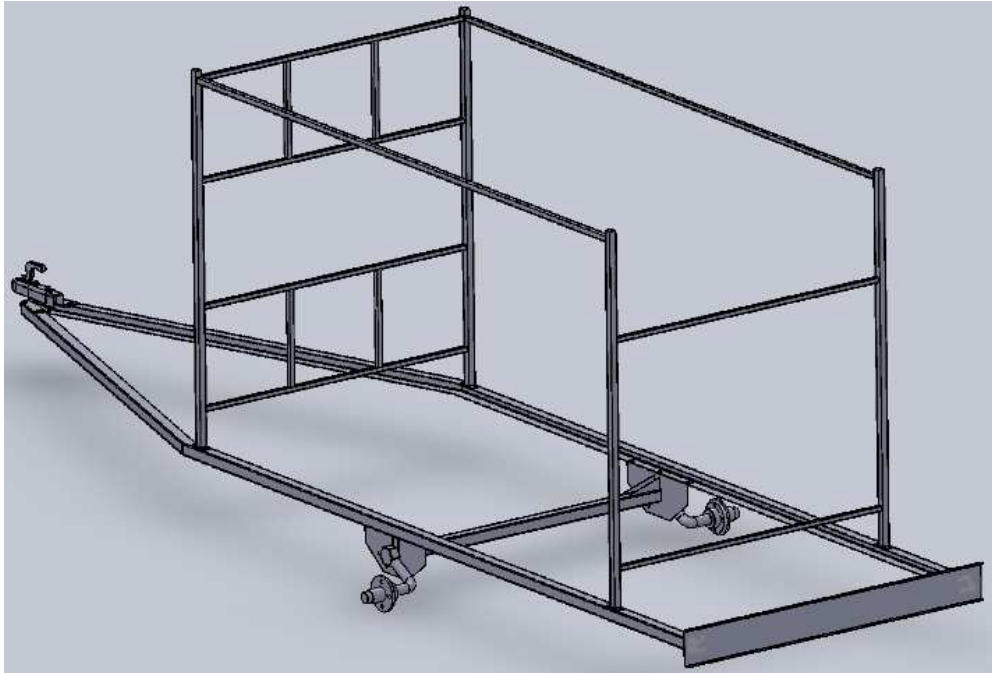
Konstrukční návrh přívěsu + konstrukce na kanoe – varianta 1. Celkový pohled.
